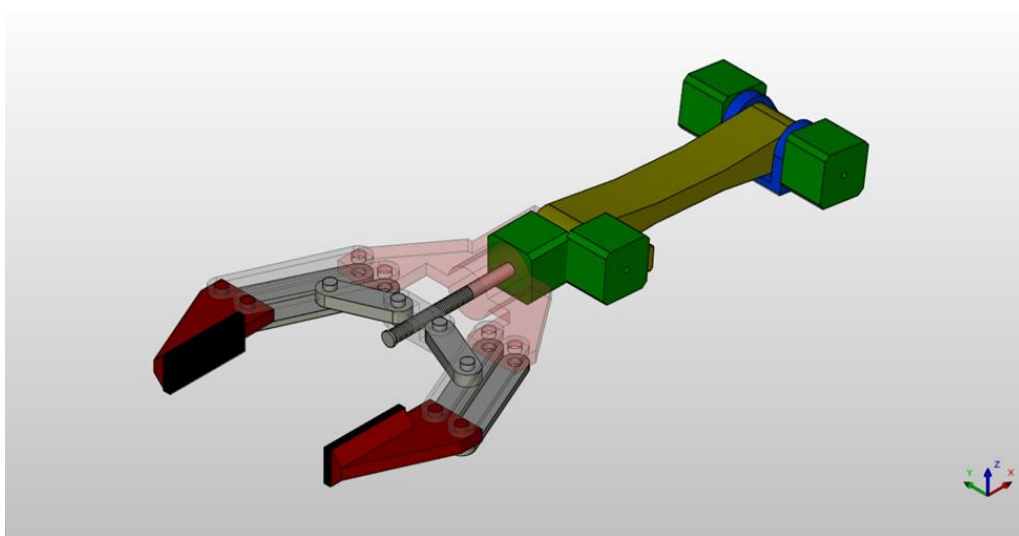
Вид в разрезе, демонстрирующий внутреннюю компоновку и рычажный механизм
